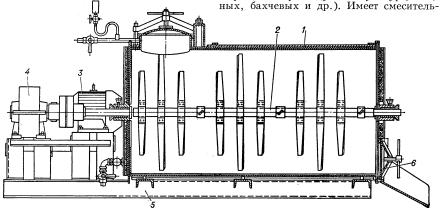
Смеситель — запарник кормов: 1 — котёл с паропроводом; 2 — лопастный смеситель; 3 — электродвигатель; 4 — редуктор; 5 — рама; 6 — разгрузочный люк.
